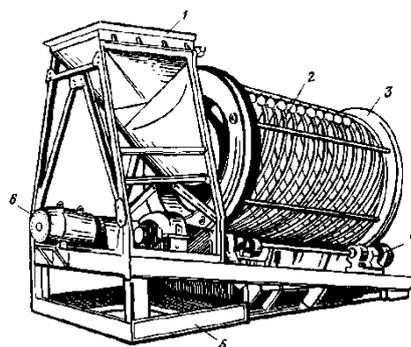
Барабанный грохот со спиральными колосниками: 1 – питающий бункер; 2 – спиральные колосники; 3 – опорный бандаж; 4 – опорный приводной каток; 5 - электродвигатель; 6 – рама
